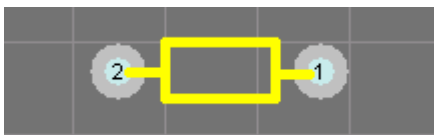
完成的 PCB 元件封装“AXIAL-0.2”
